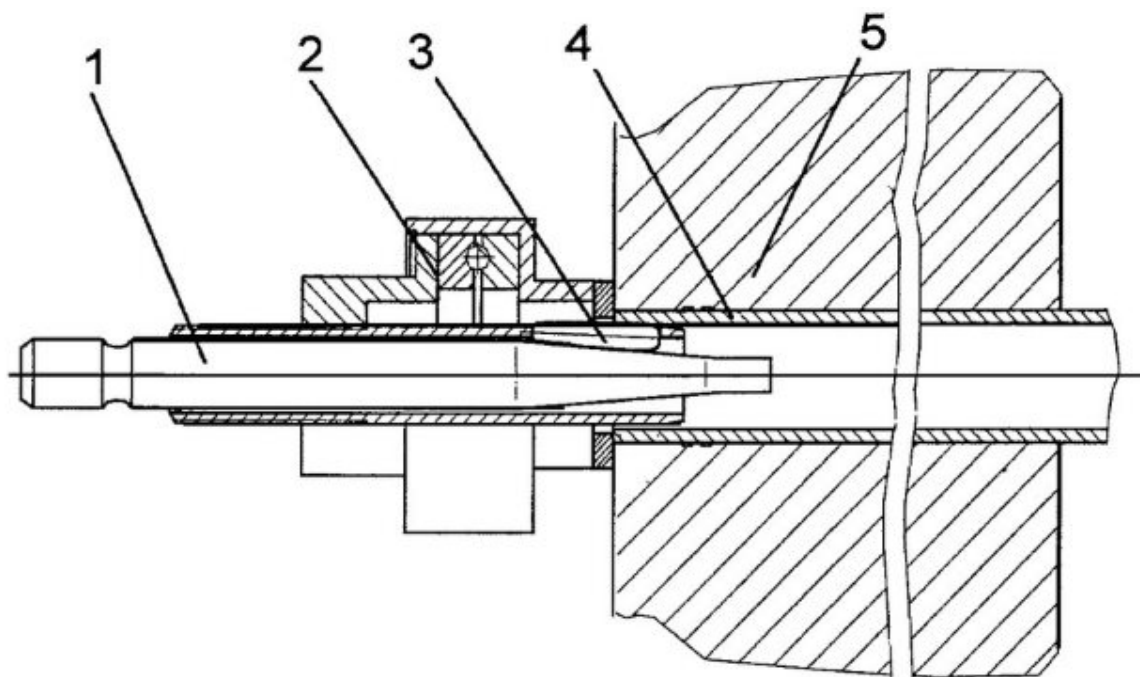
Крепление трубы с помощью роликовой вальцовки: 1 — веретено, 2 — втулка с подшипником, 3 — ролик, 4 — труба, 5 — трубная доска
